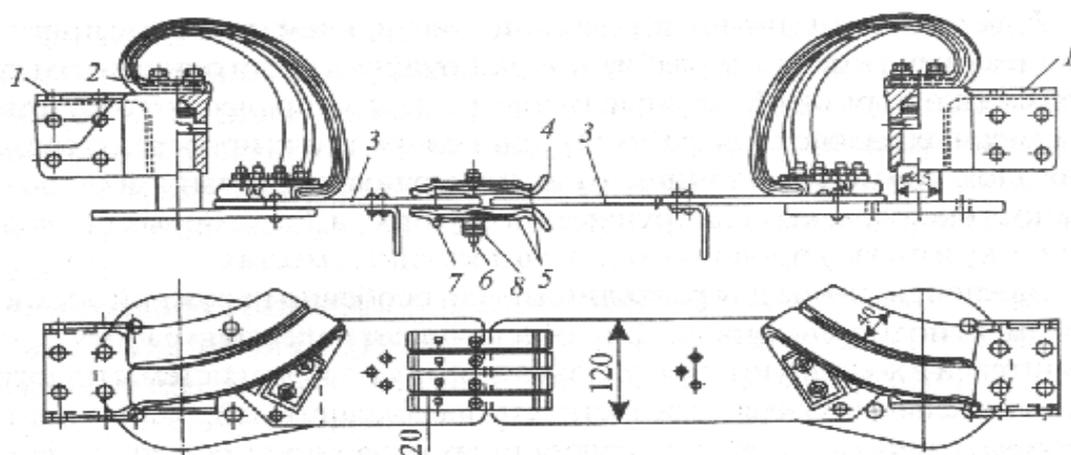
Токоведущая система горизонтально-поворотного разъединителя: 1 — зажим; 2 — гибкая связь; 3 — пластина пожа; 4 — ламель; 5 — стальные пластины; 6 — шпилька; 7 — фиксирующий болт; 8 — пружина
